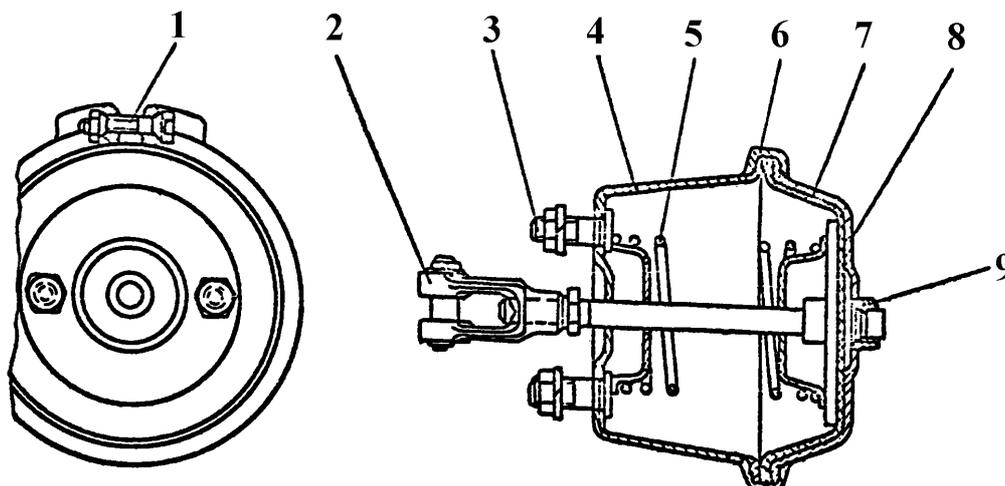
Камера тормозная: 1 – стяжной болт; 2 – вилка; 3 – болт; 4 – корпус; 5 – пружина; 6 – хомут; 7 – диафрагма; 8 – крышка; 9 – штуцер
